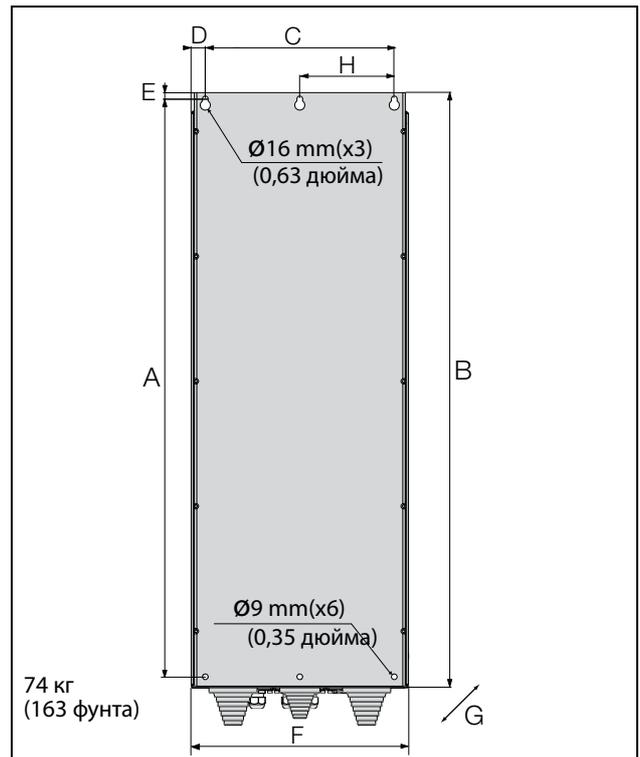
Устройство Emotron FDU моделей с 48-210 по 295 (размер корпуса F), Устройство Emotron FDU моделей с 69-82 по 200 (размер корпуса F69).
